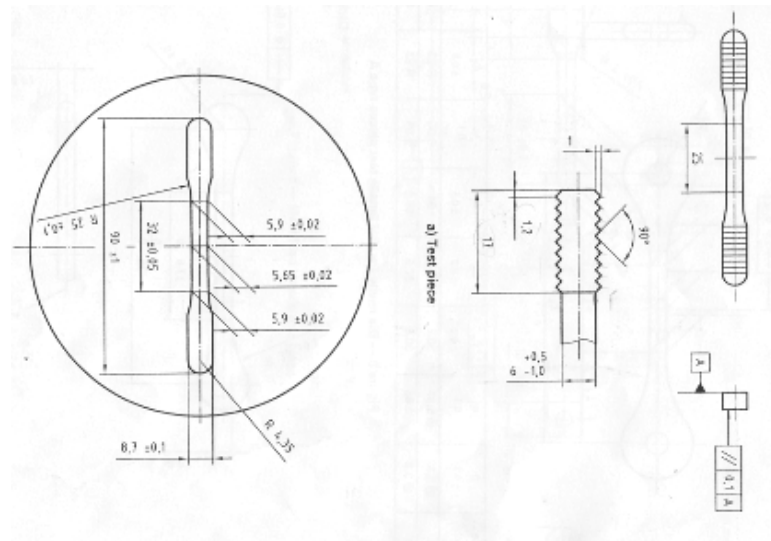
Dimensione stampi: qui sopra stampo per barrette e per cilindri; a fianco e sotto, stampi ossi.
